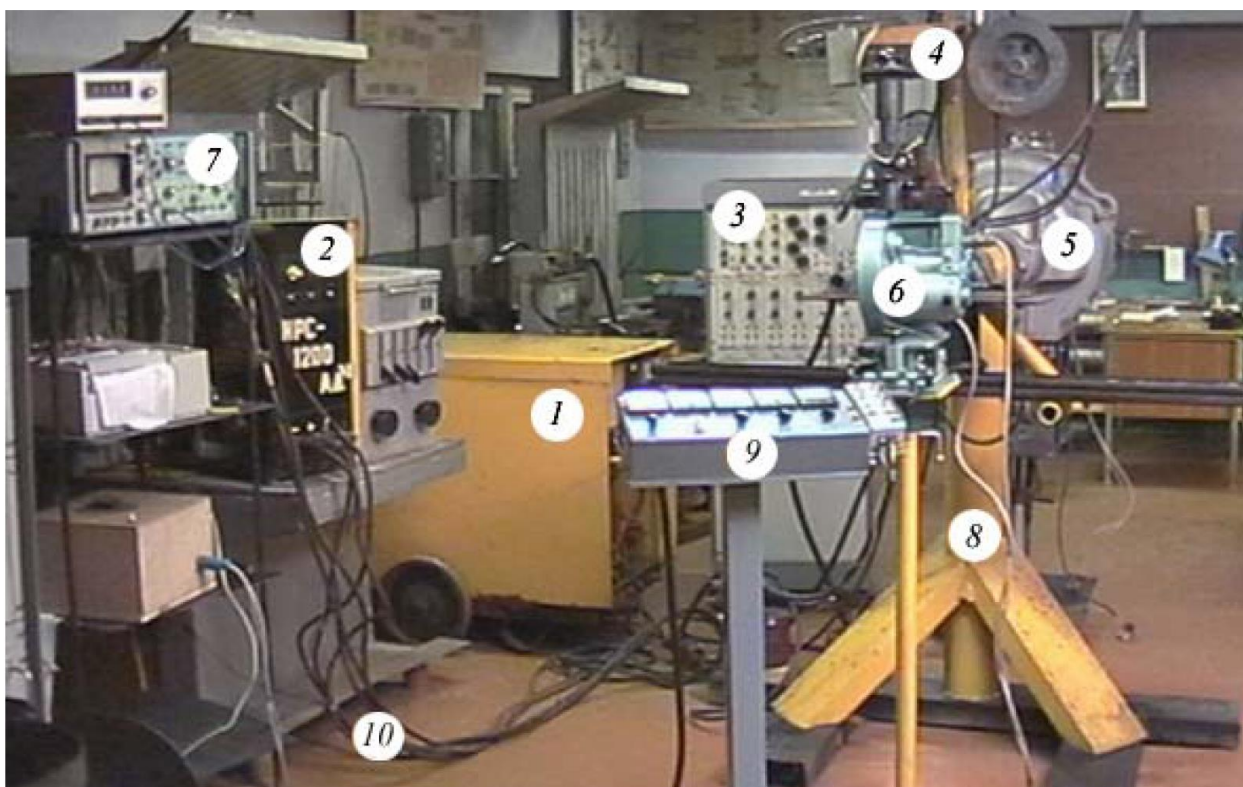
Исследовательский комплекс для формирования импульсного режима сварки
